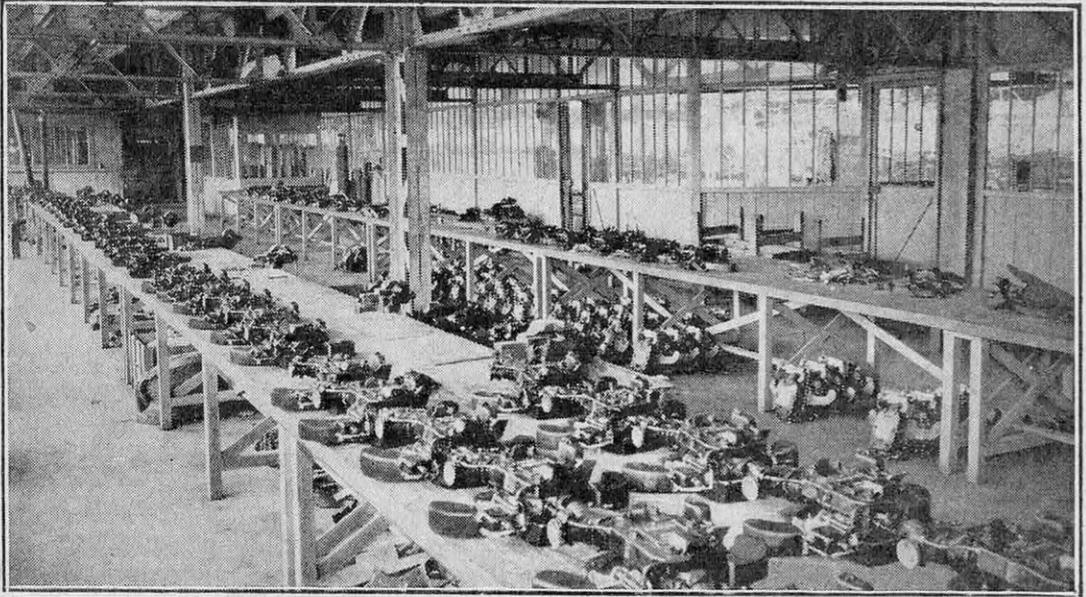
UNE CHAÎNE DE MONTAGE DU CARBURATEUR CHIMIQUE PENDANT SA FABRICATION
